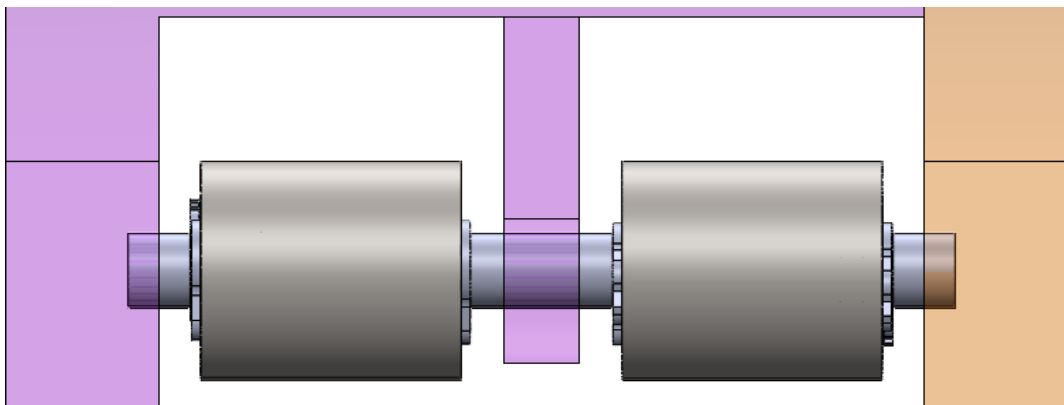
Vista detalle del interior del carrete (Fuente 27)
